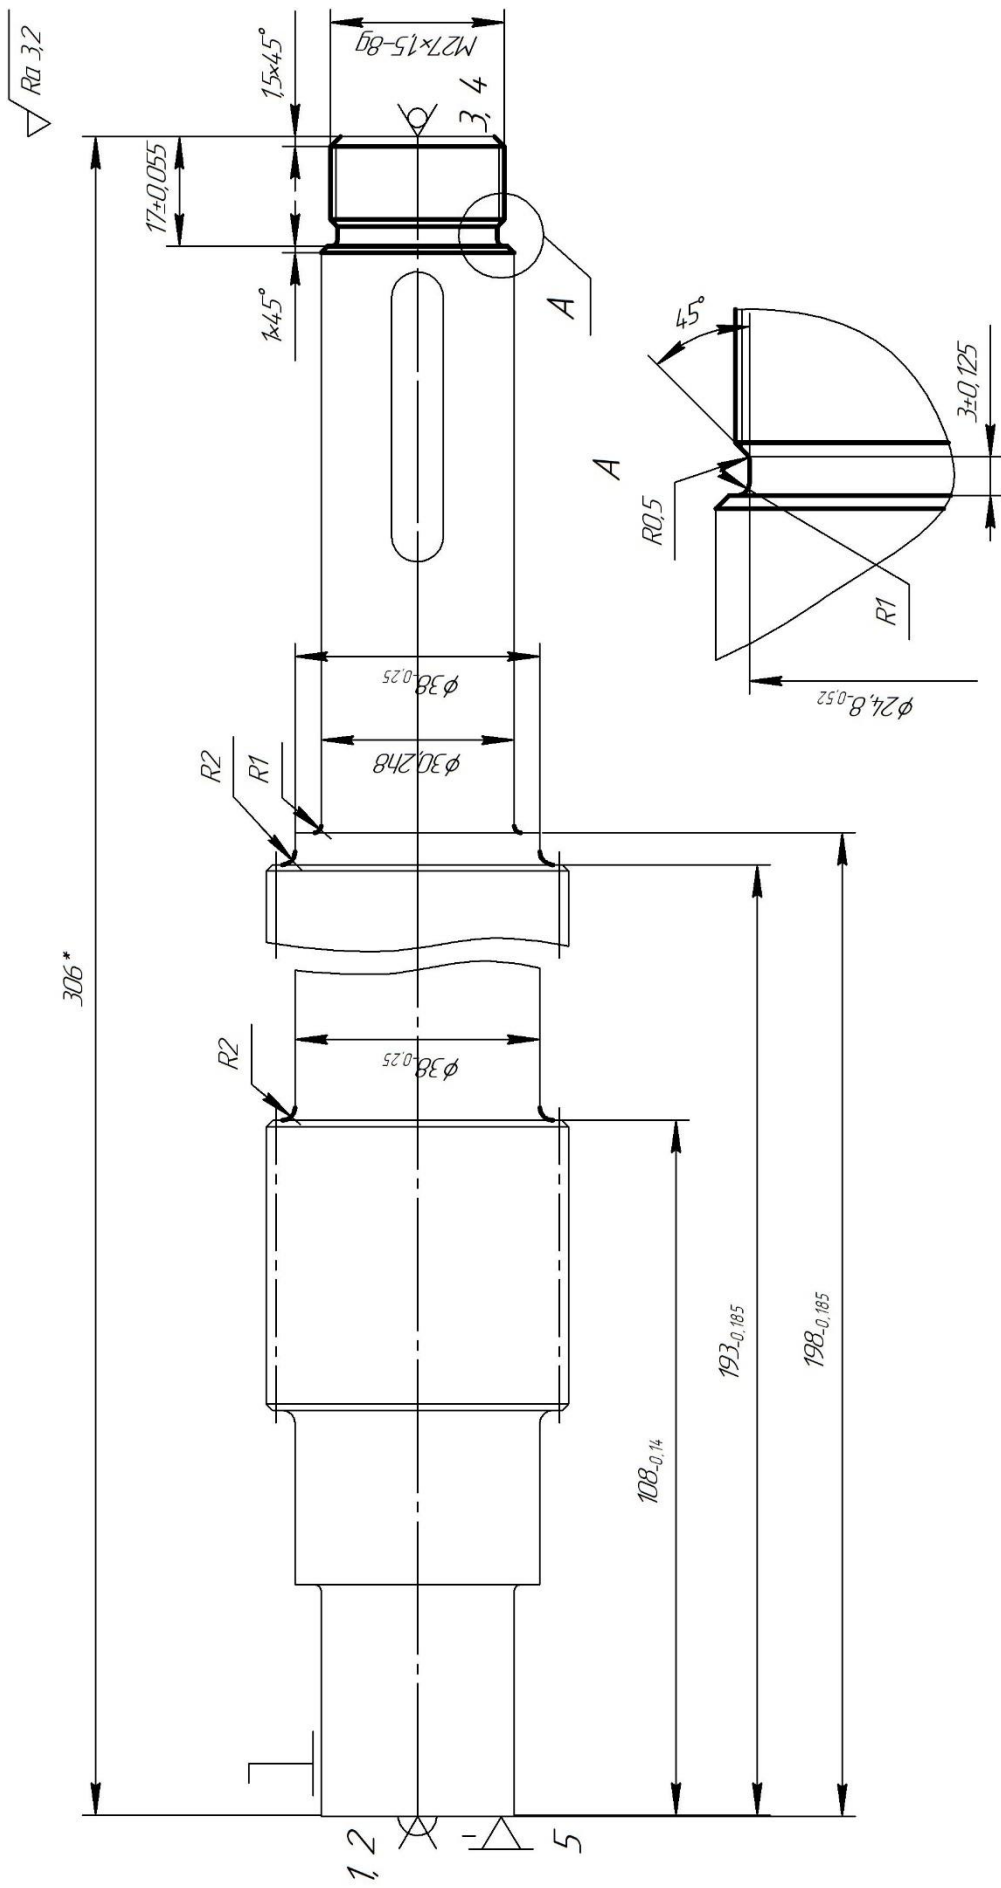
Схема базування заготовки на операції 065 токарній з ЧПК, установ А
